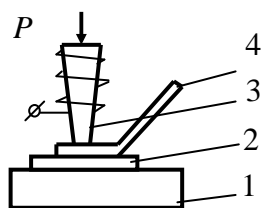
Схема термокомпрессионной сварки: 1 – рабочий стол; 2 – подложка с тонкой пленкой; 3 – инструмент с нагревателем; 4 – проволочный проводник
